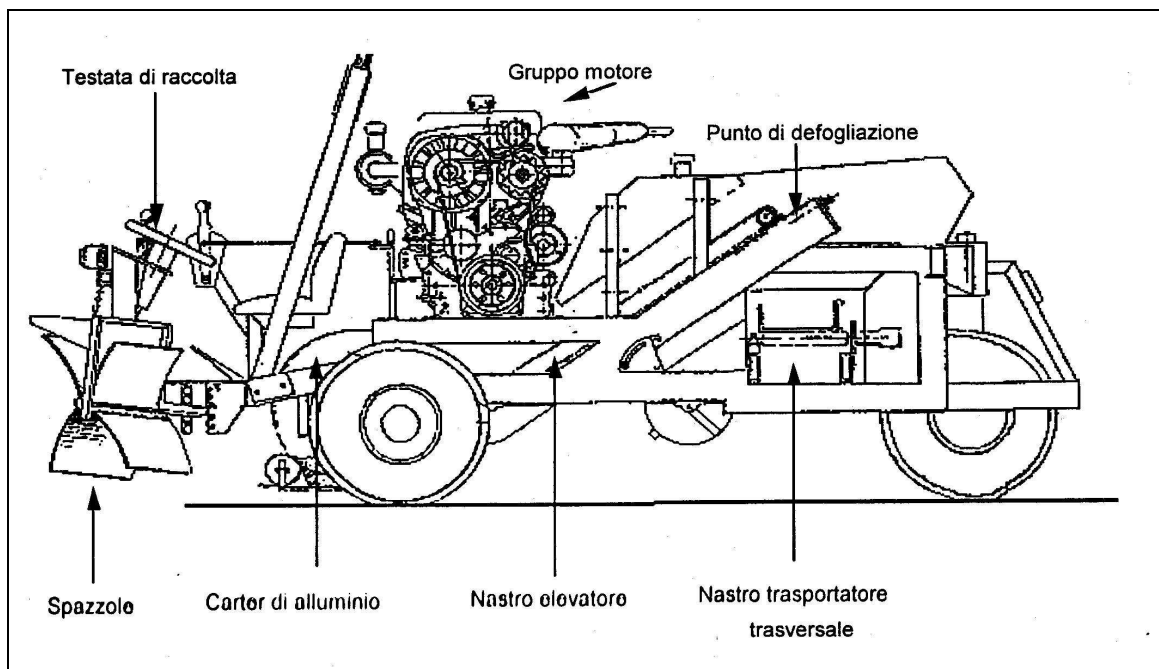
Vista in sezione della raccattrice Perla 55/ 4
